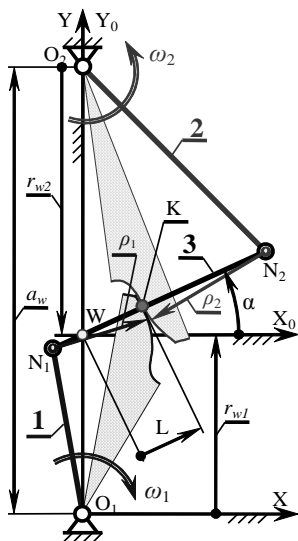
Цилиндрическая передача и рычажный заменяющий механизм
